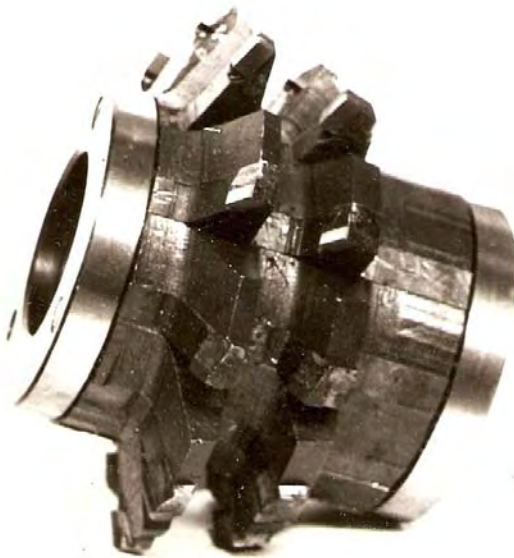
Рабочая конструкция правого корпуса двухкорпусной фрезы $m=16\text{мм}$ со вставными зубчатыми рейками.
